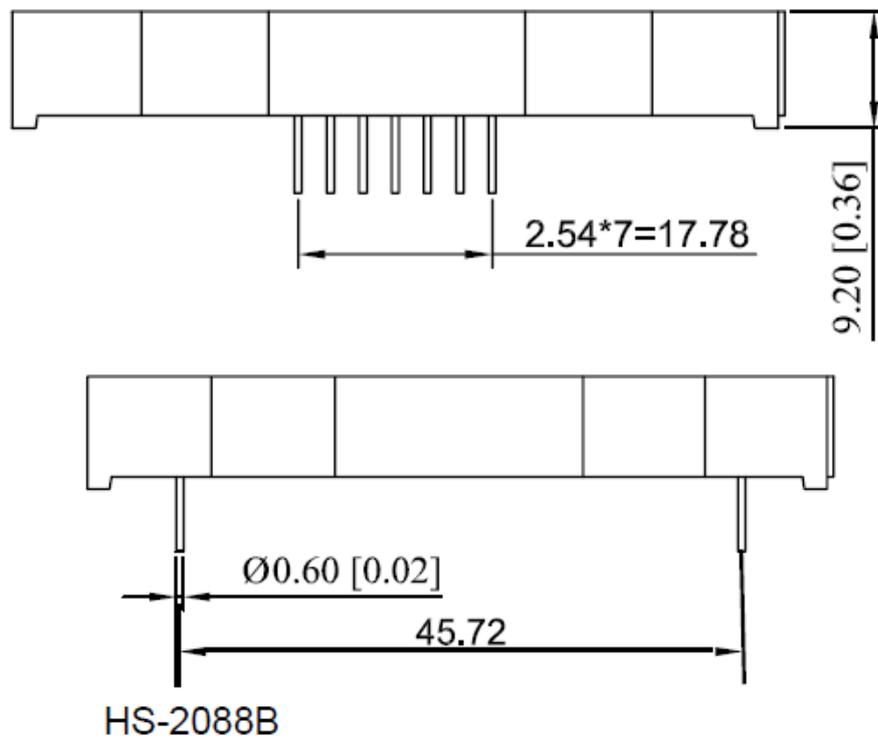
(b) : Dimensions de la matrice HS2088B
